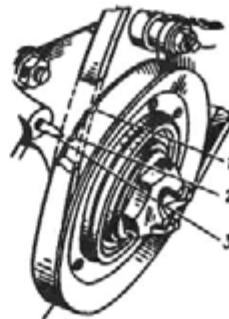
Положение риски на шкиве коленчатого вала в момент нахождения поршня первого цилиндра в в.м.т.:
